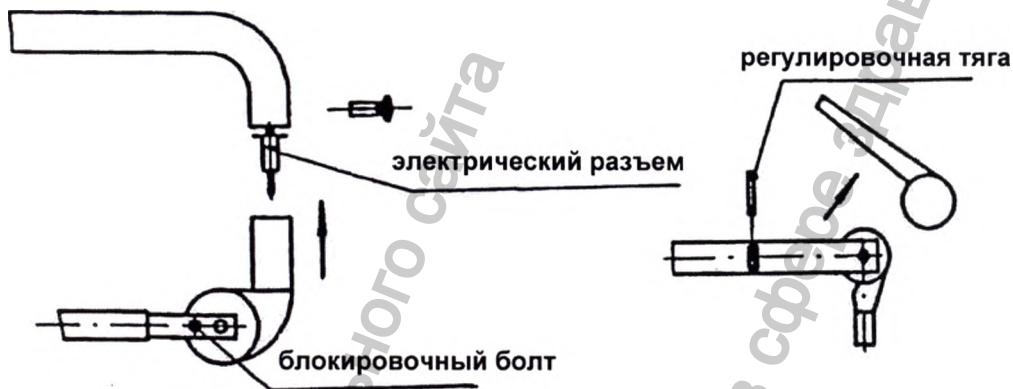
Установка балансировочной части 1 Рис.9 Установка балансировочной части 2
